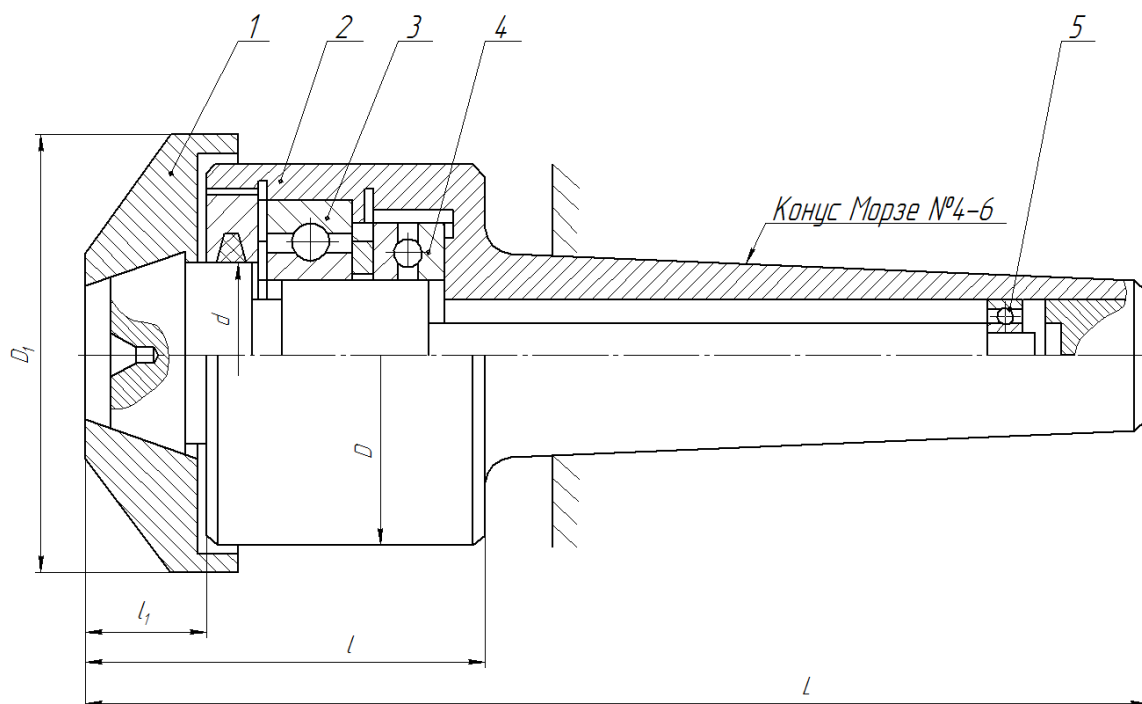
Будова обертвого центра для порожніх деталей: 1 – центр; 2 – корпус; 3, 5 – радіальний підшипник; 4 – упорний підшипник
